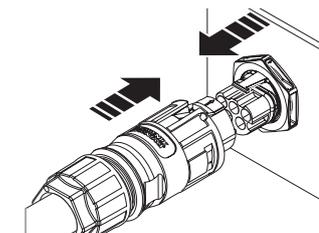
AC-Anschlussstecker mit dem Gerätestecker einrasten
